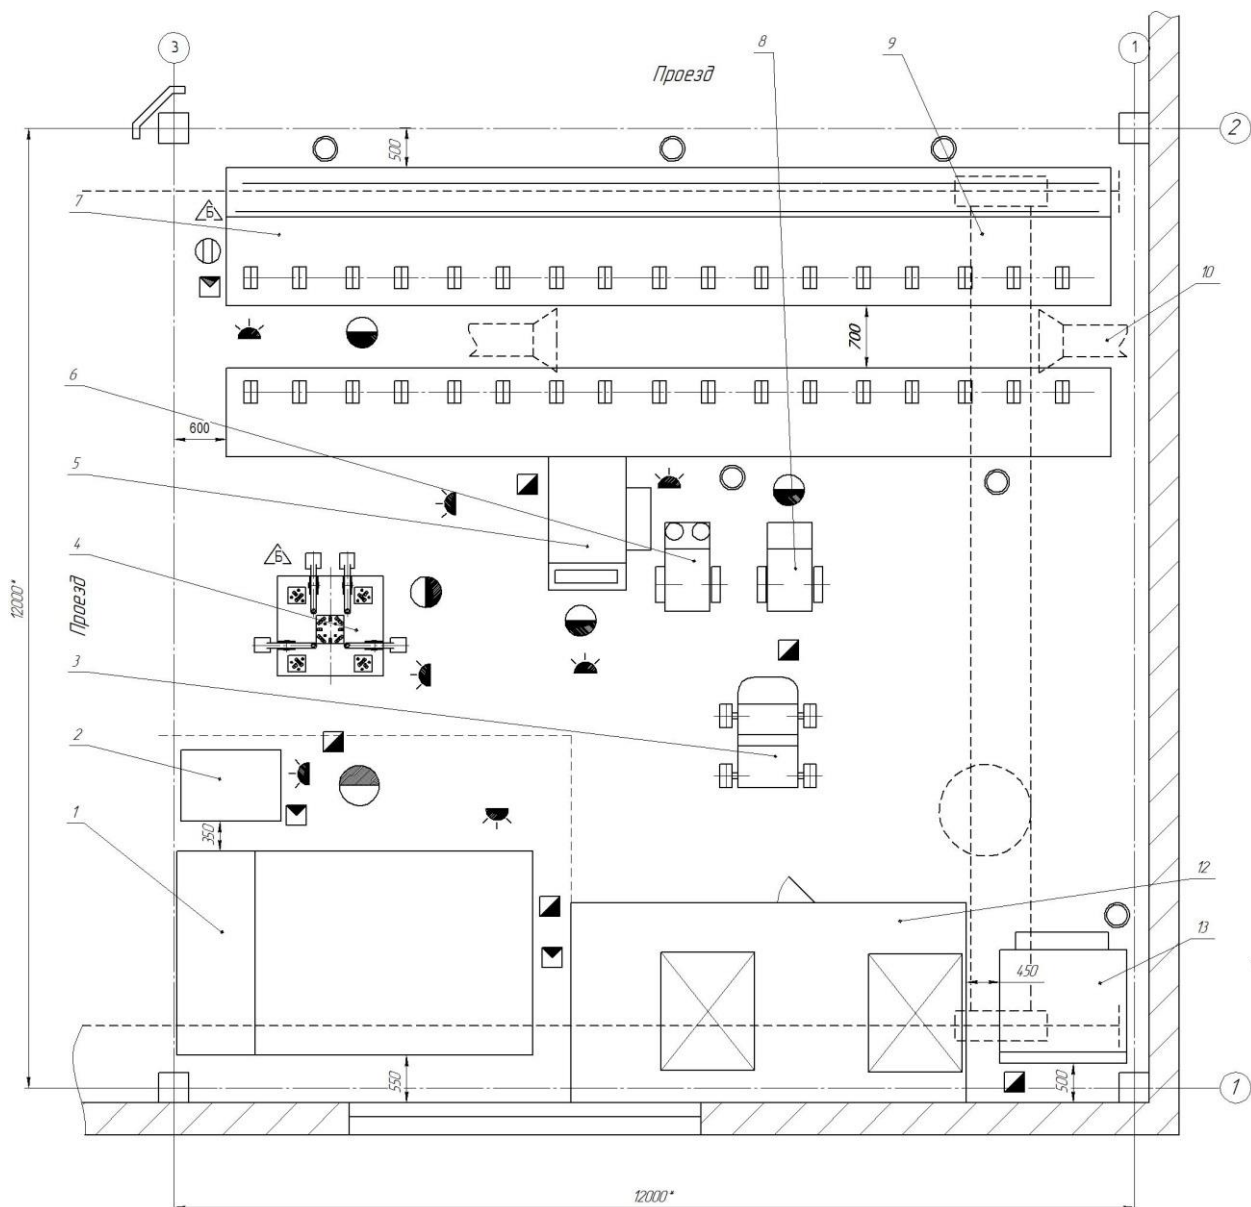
Участок для сборки и сварки элементов перехода через трубопровод
